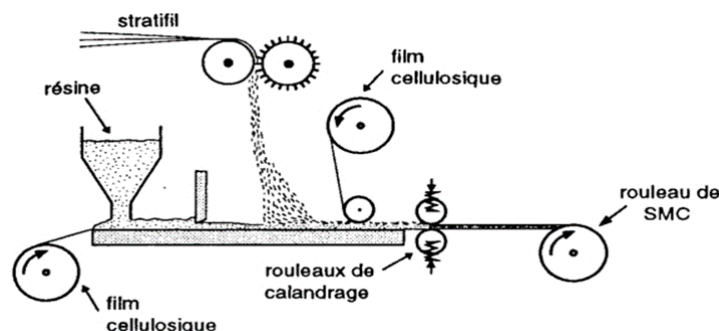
Moulage par compression thermodurcissable SMC [3]
